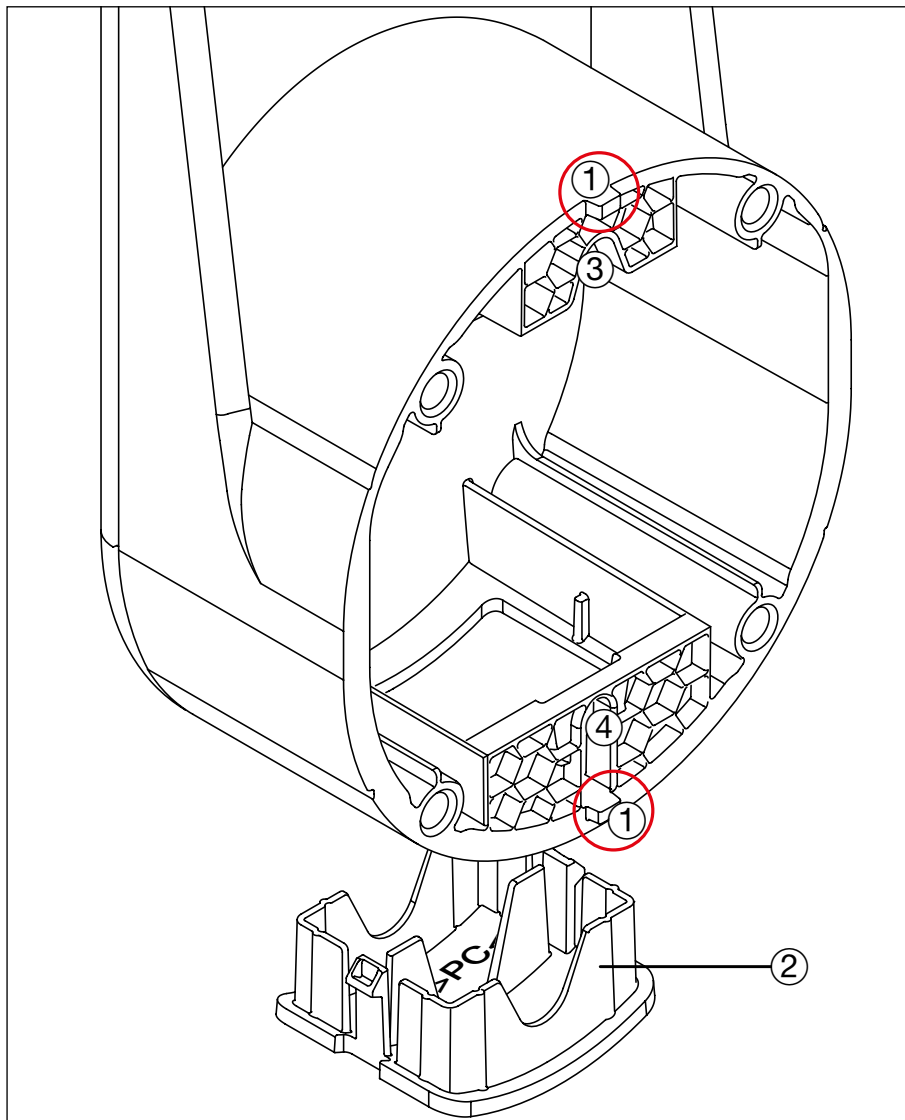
Montage du porte-câbles sur un mur (vue de la face arrière)
